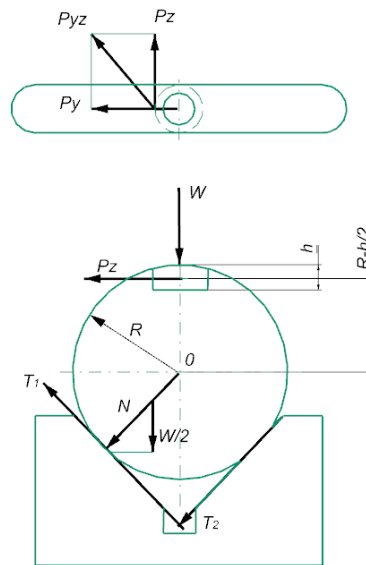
Схема сил при фрезеруванні шпоночного паза
